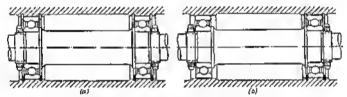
Fijación de un árbol en cojinetes de contacto rodanto
